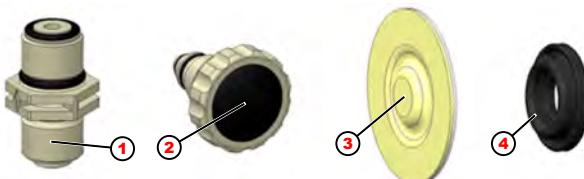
Ensemble de pièces d'usure à 5 l/h et 11 l/h
